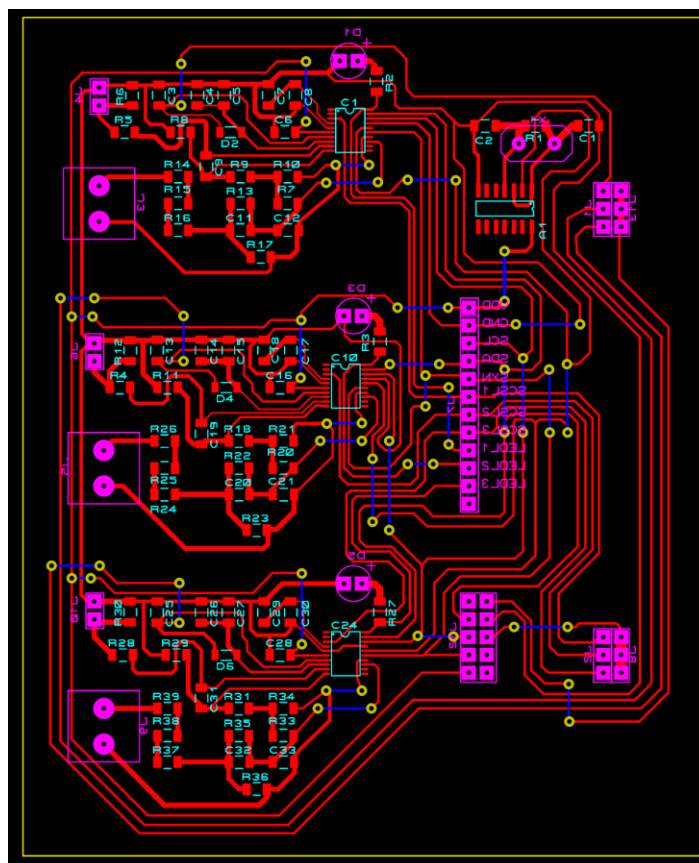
PCB, dimensiones ancho: 9.65 cm, largo: 11.93 cm
